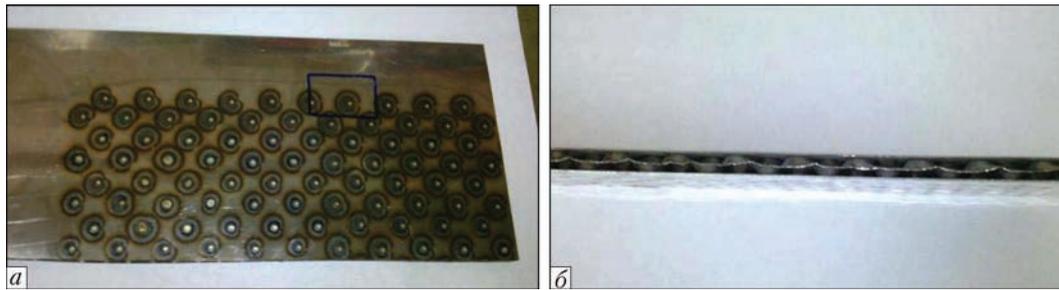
Изображение трехслойного образца с двойной точечной сваркой: *а* – вид сверху; *б* – вид с торца
